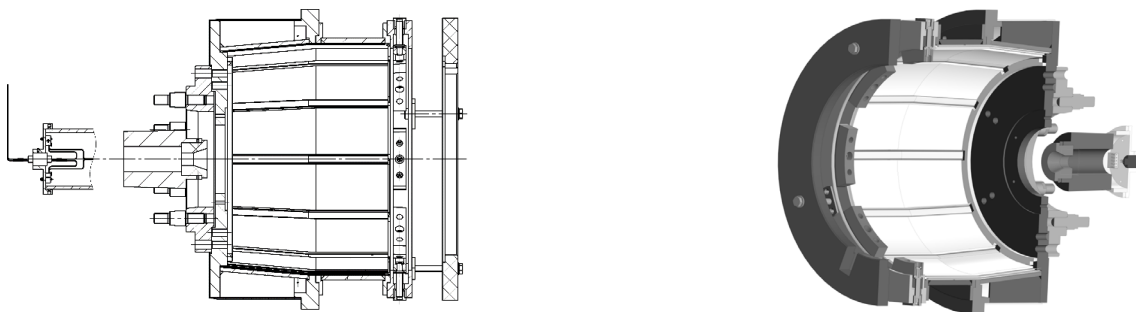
Схема и внешний вид в сечении доработанного барабана станка с ЧПУ
